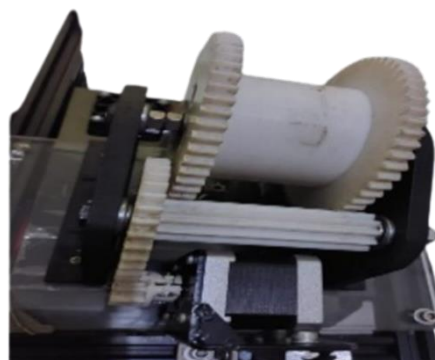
Konfigurasi *compound gear* pada sistem transmisi (*gear A–D*).
